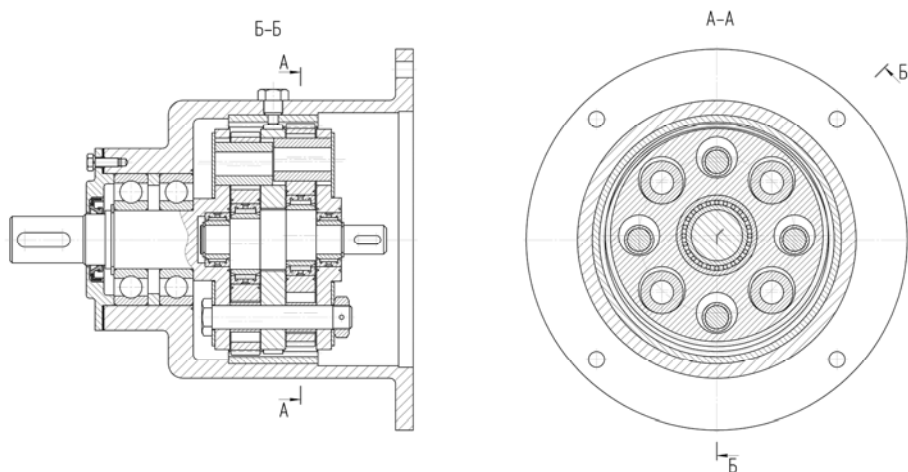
Конструкция передачи типа $K-H-V$ с цилиндрическими роликами механизма снятия движения с сателлита
